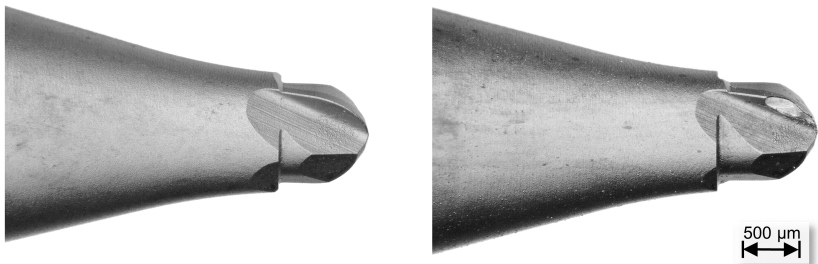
Mikrofräs Werkzeug vor (links) und nach (rechts) der vollständigen Modifikation eines beschichteten Wendelbohrers
